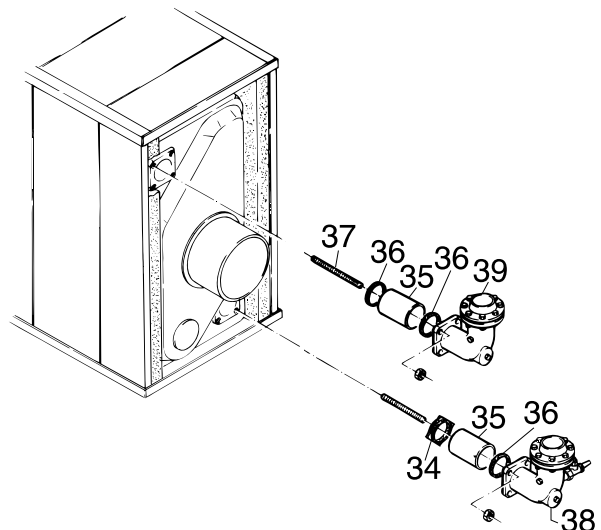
Montage Distanzstücke und Anschlußkrümmer. Gewindebolzen (37) je 4 Stück oben und unten einschrauben. Dichtungen (36) und Abdichtplatte (34) zusammen mit Distanzstück (35) anpassen. Anschlußkrümmer (38) und (39) mit den Mutter befestigen.
